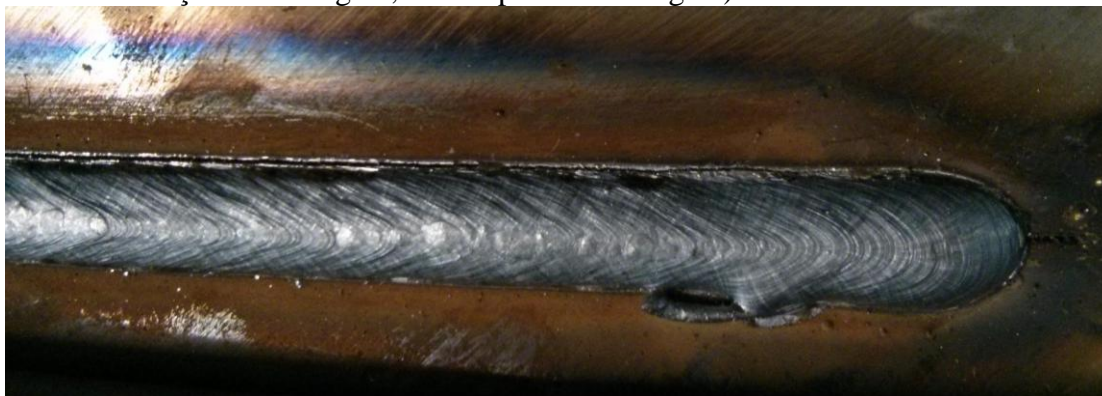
Experimento M3 mostrando uma trinca na região marginal direita do cordão de solda (referente à direção de soldagem, lado superior na imagem).
